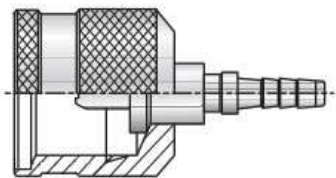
Приспособление для дренажа гидроцилиндра
